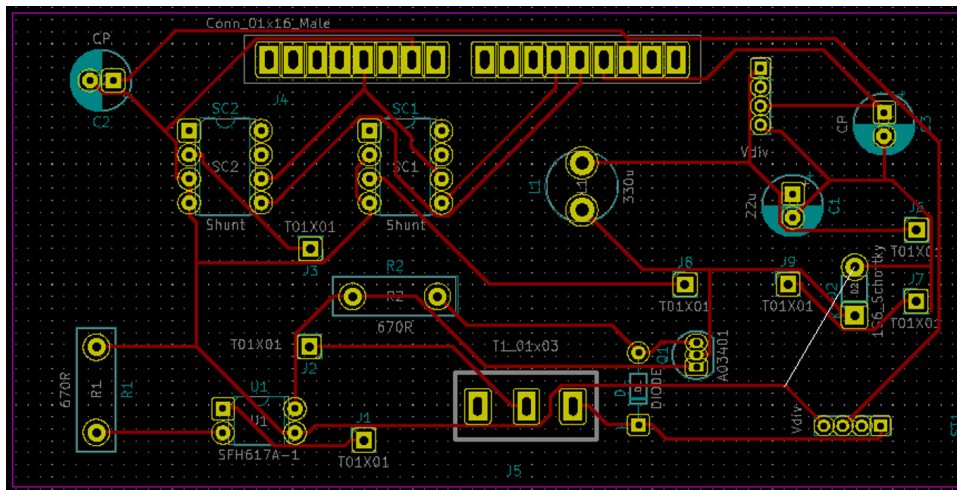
PCB Conversor Buck.Fonte: o autor.
